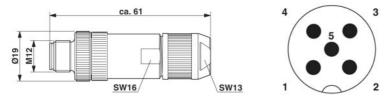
Stecker M12 x 1 gerade, geschirmt; Polbild Stecker M12, 5-polig, A-kodiert, Ansicht Stiftseite,
